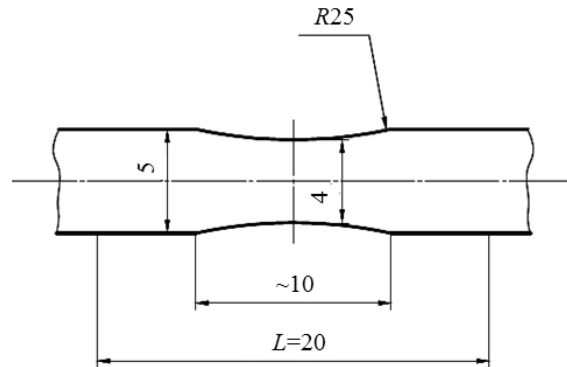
Форма корсетной части доработанных образцов из подшипниковой стали
